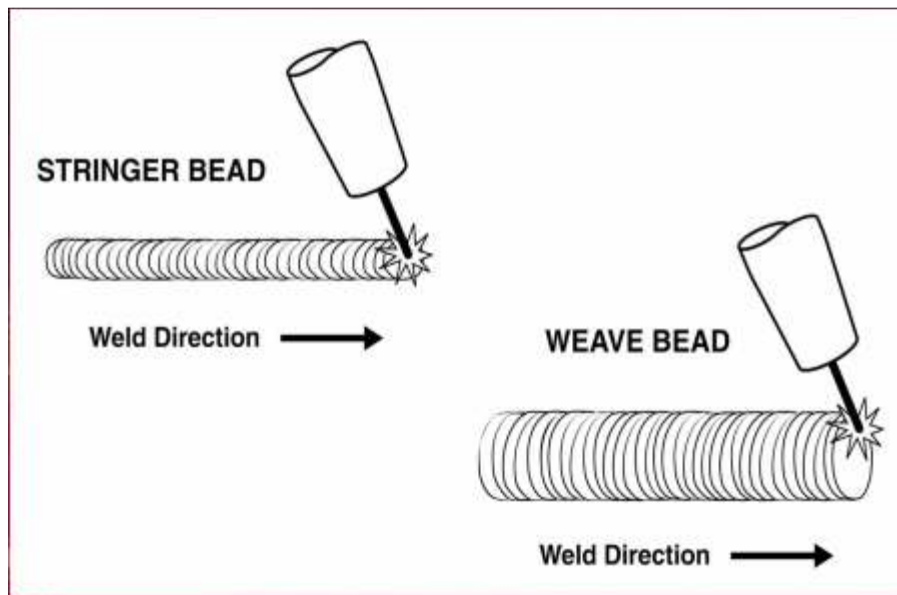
Esquematzación de las Técnicas de soldadura para el Proceso MIG-MAG Lincoln Soldaduras de Colombia, presentación (2007). p. 33.
